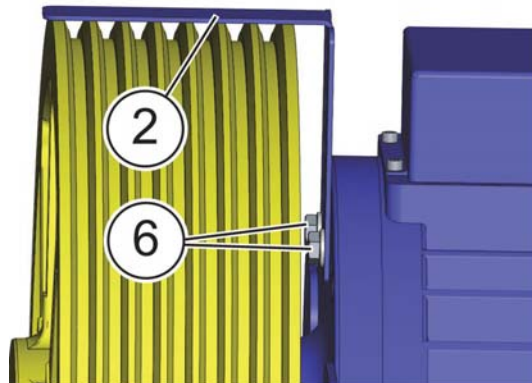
Variantes de montage 3ème protection contre le rebond des câbles
